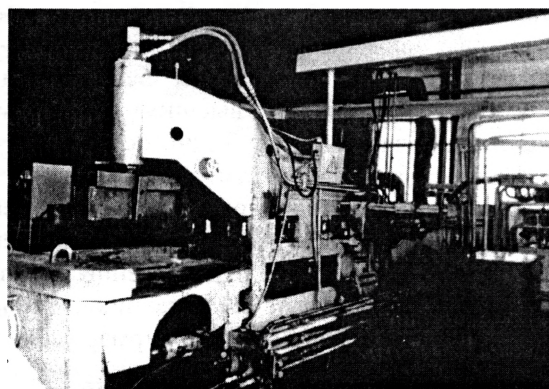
Полуавтоматическая линия для прокатки малолистовых рессор
